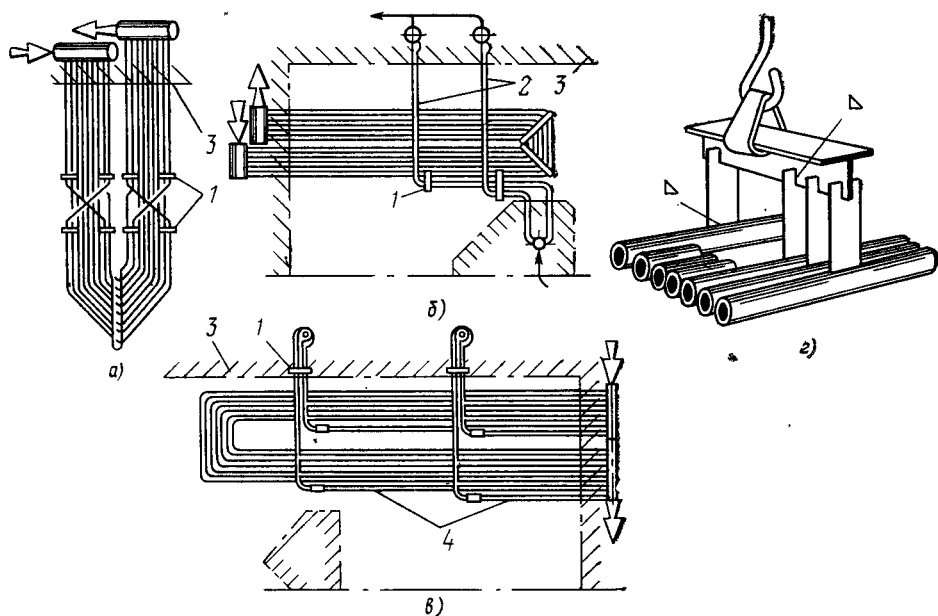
Различные конструкции крепления ширм и потолочных труб пароперегревателя.
